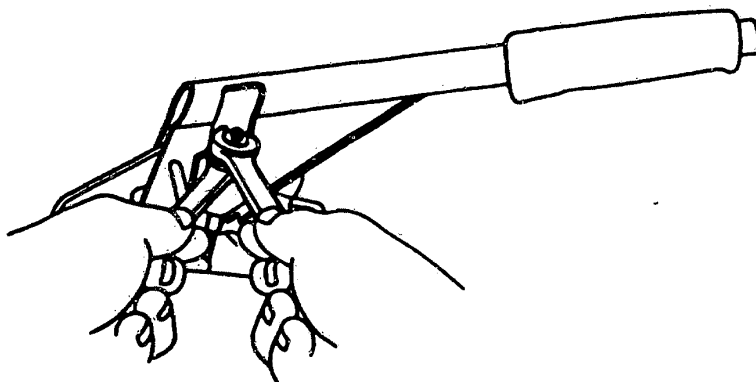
Die Einstellschraube der Handbremse befindet sich neben dem Handbremshebel.
